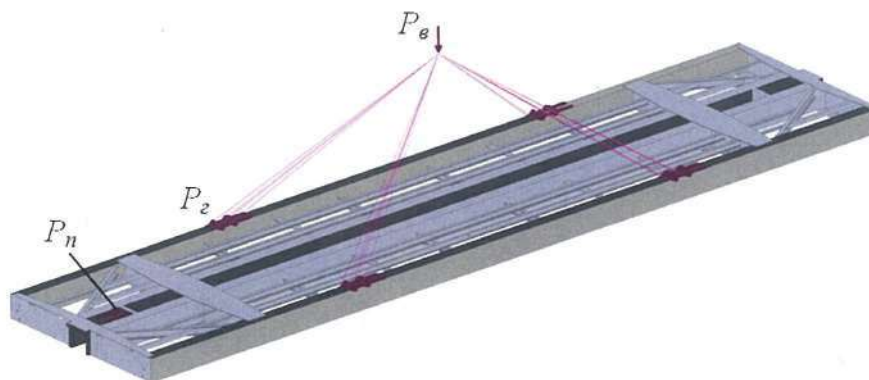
Розрахункова схема несучої конструкції вагона-платформи
